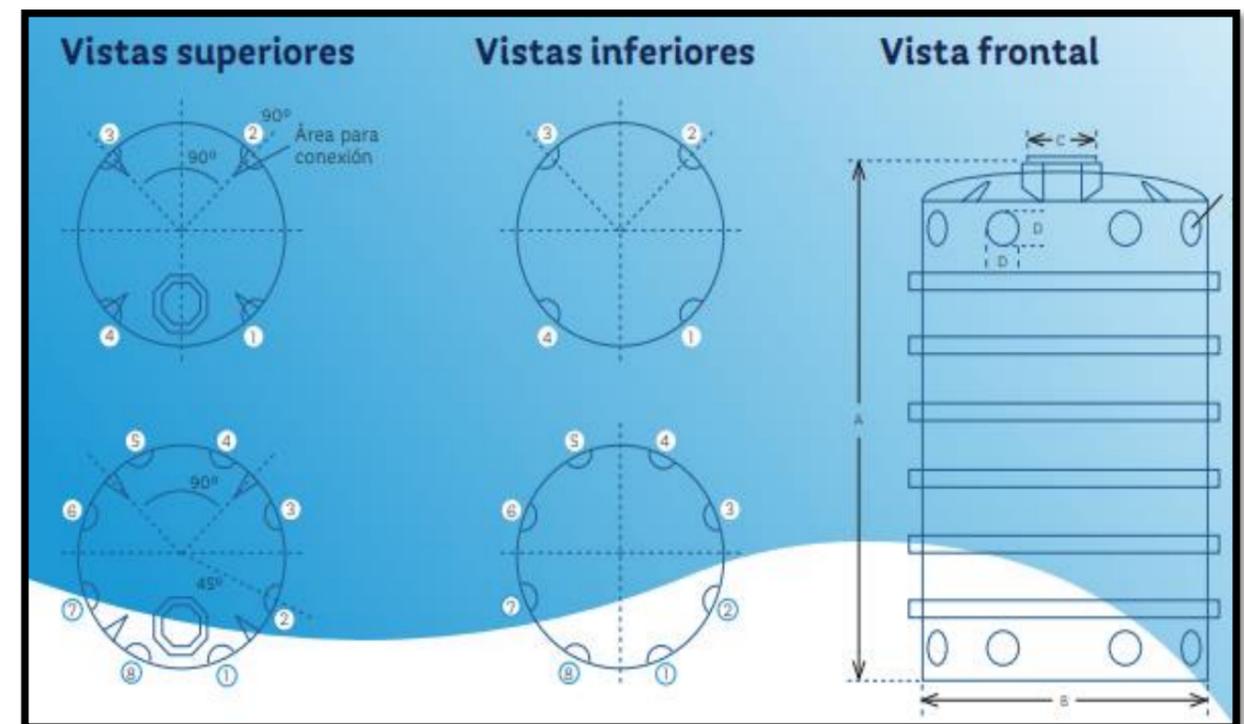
Ficha técnica de Tanque Rotoplas de 10,000 Lts. Fuente: Rotoplas Centroamérica.
